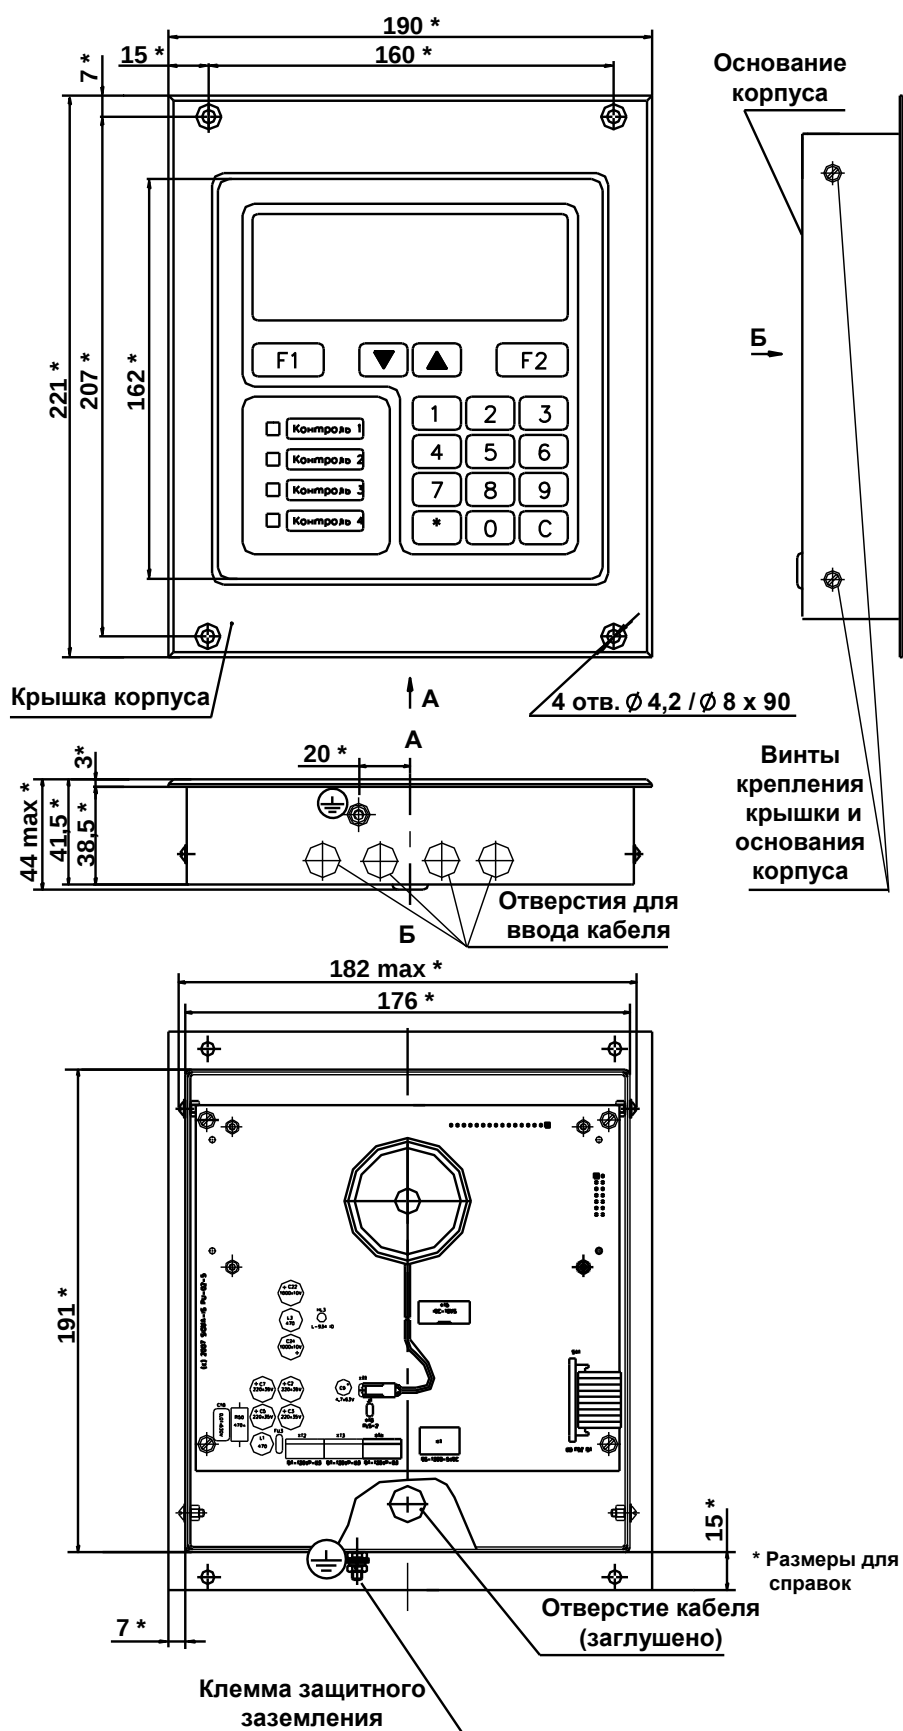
Габаритные и присоединительные размеры (врезное исполнение Тип 2)
